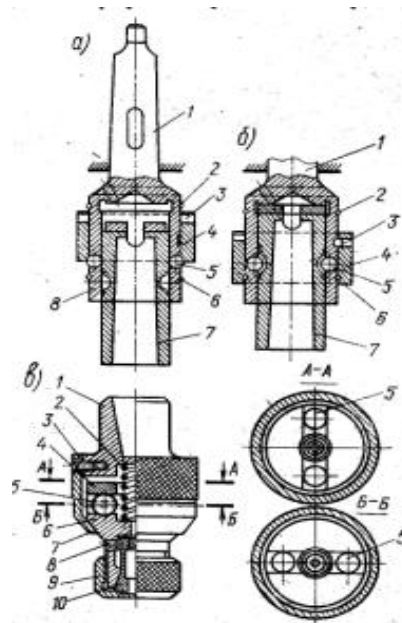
Швидкозмінні патрони для установки і затиску свердл, зенкерів, розгорток (а, б) і самоцентруючий патрон для закріплення мітчиків (в)
